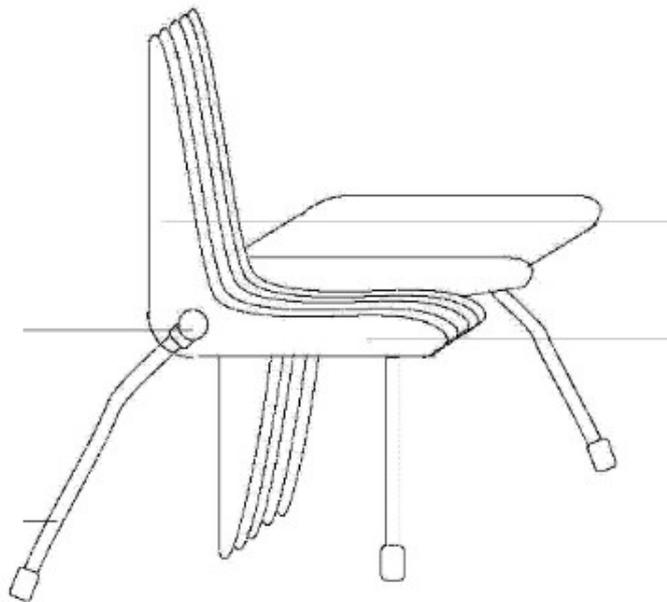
Table-chair integrated machine. Fuente Espacenet
